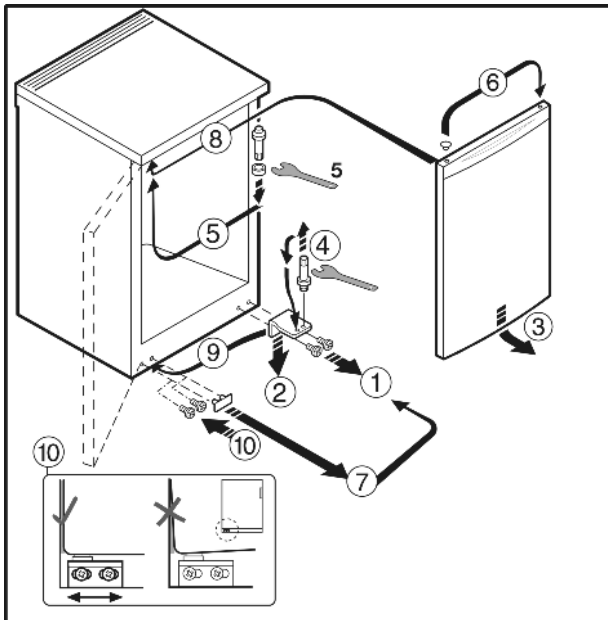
Laitteet, joissa ei ovenkahvaa
